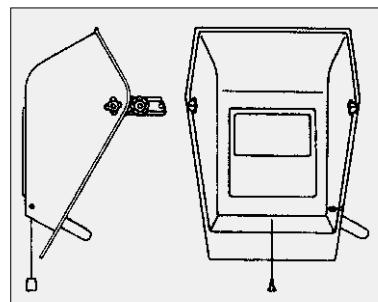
Сварочный щиток с подвижным светофильтром ННП-С-505 У1
